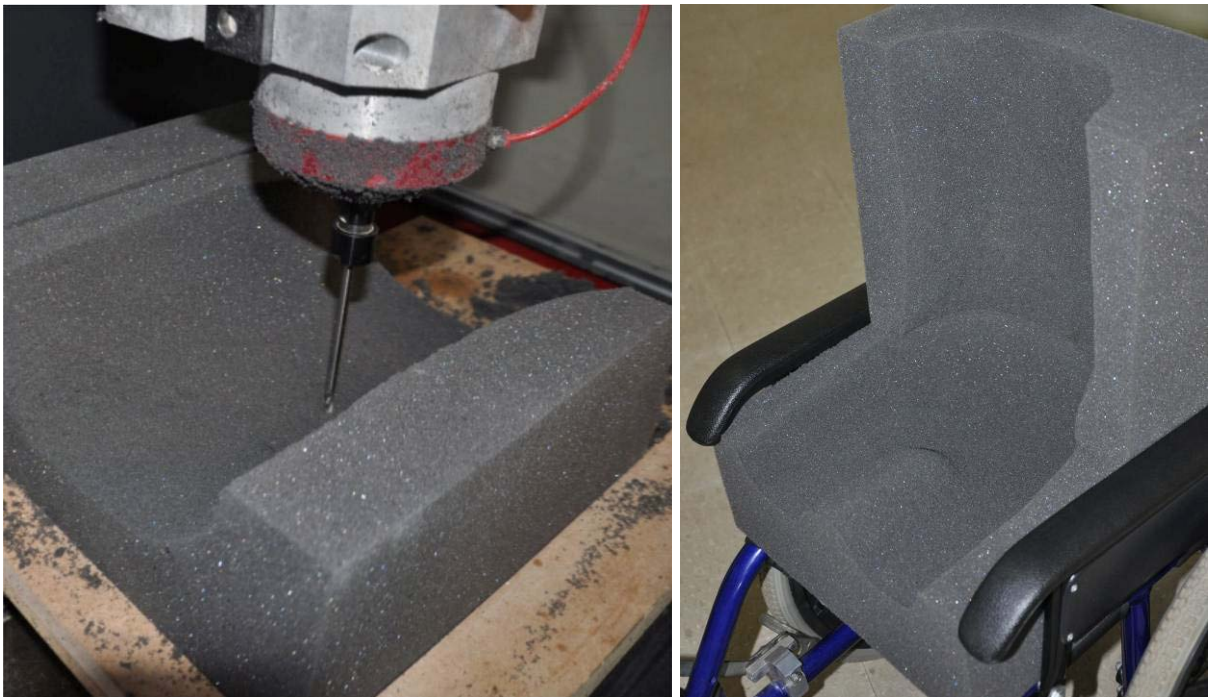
Usinagem CNC do encosto e assento completo usinado do usuário A.
